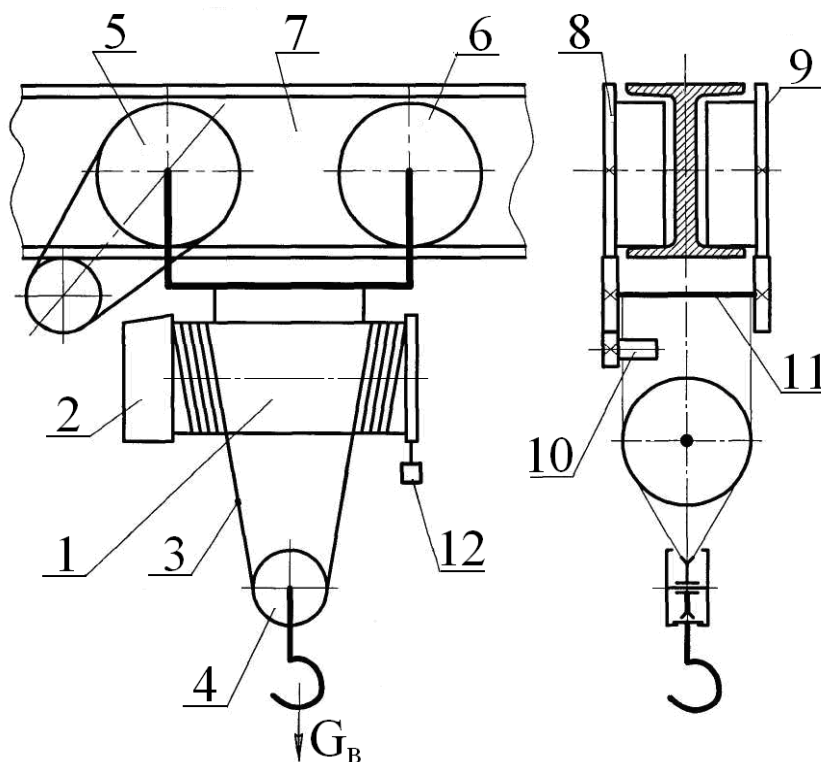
Принципова схема талі з електроприводом: 1 – барабан з електродвигуном; 2 – редуктор; 3 – канат; 4 – крюкова підвіска; 5 – ведуче колесо; 6 – ведене колесо; 7 – траверса; 8 – редуктор лівий; 9 – редуктор правий; 10 – електродвигун; 11 – проміжний вал; 12 – пульт
